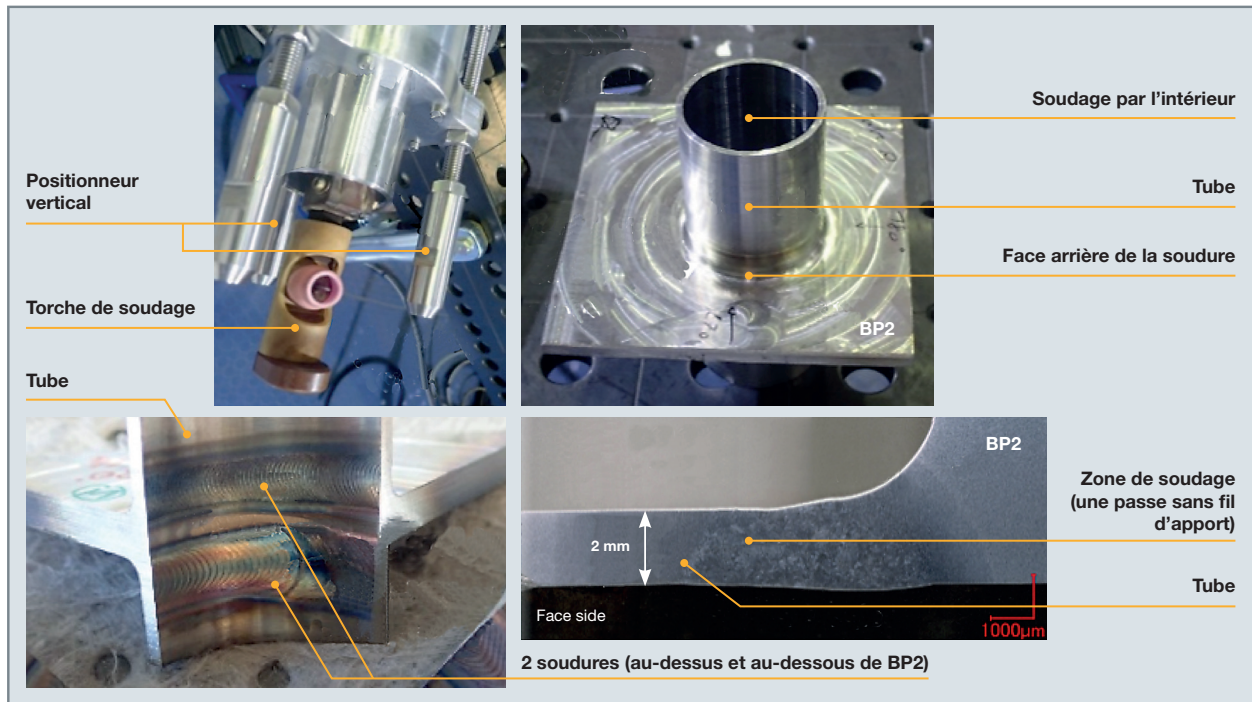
Équipement de soudage TIG orbital (a), face envers de la soudure He/BP2 (b), face endroit de la soudure He/BP2 (c) et coupe transversale (d).
